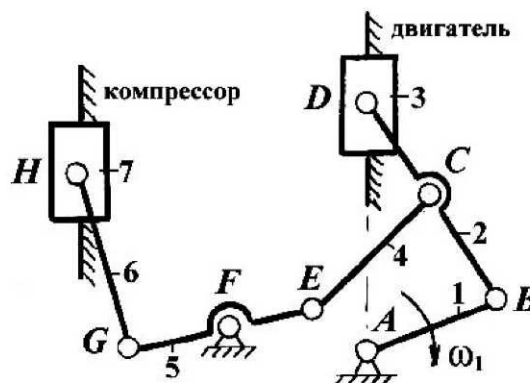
Механизм компрессорного двигателя внутреннего сгорания
